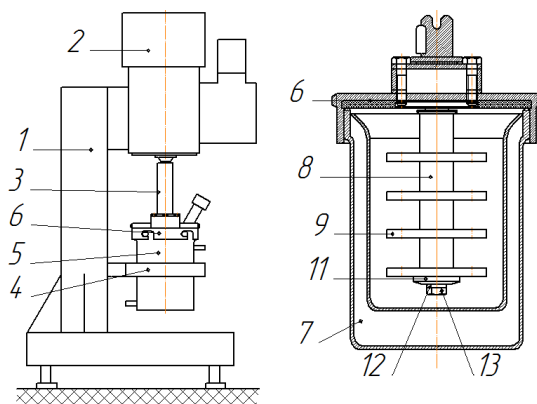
Експериментальний стенд "Бісерний млин лабораторний" (Hrininh, Gubenia, & Chepelyuk, 2021): 1 — станина; 2 — асинхронний двигун; 3 — вал двигуна; 4 — хомут; 5 — робочий стакан; 6 — кришка; 7 — сорочка охолодження; 8 — вал; 9 — диски; 10 — шпонка; 11 — шайба; 12 — шайба Гровера; 13 — болт
